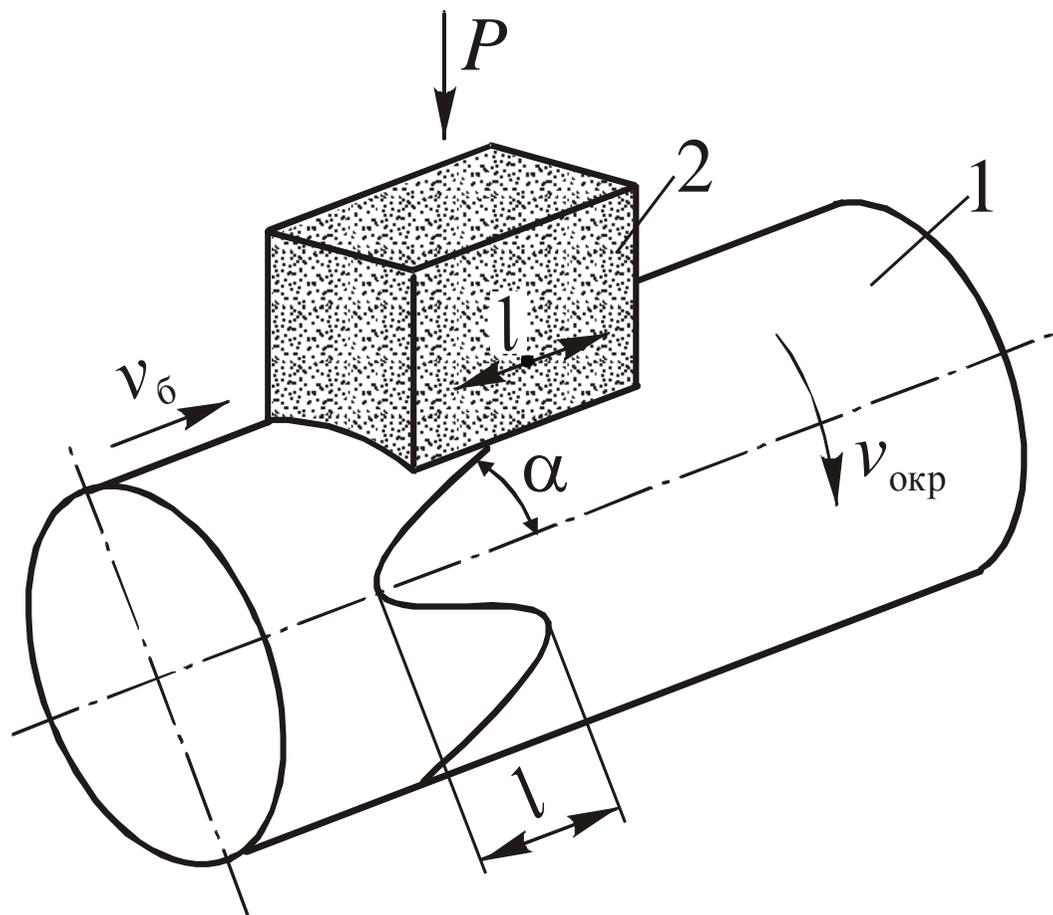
Схема суперфиниширования: 1 – заготовка; 2 – абразивный брусок
